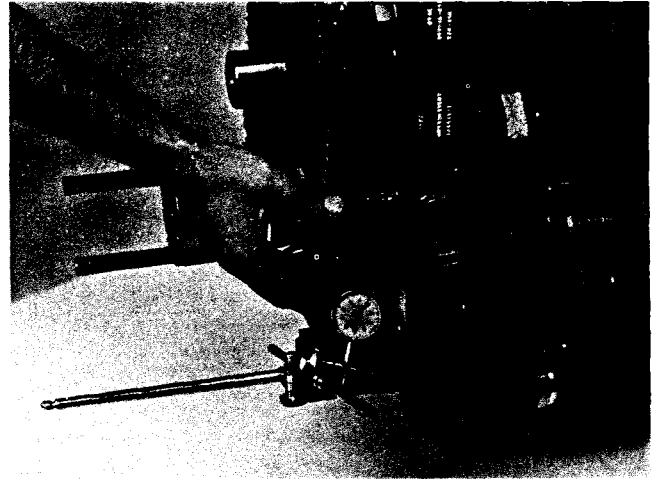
, (N114264). Revisión del juego del engranaje de la bomba de aceite lubricante.
